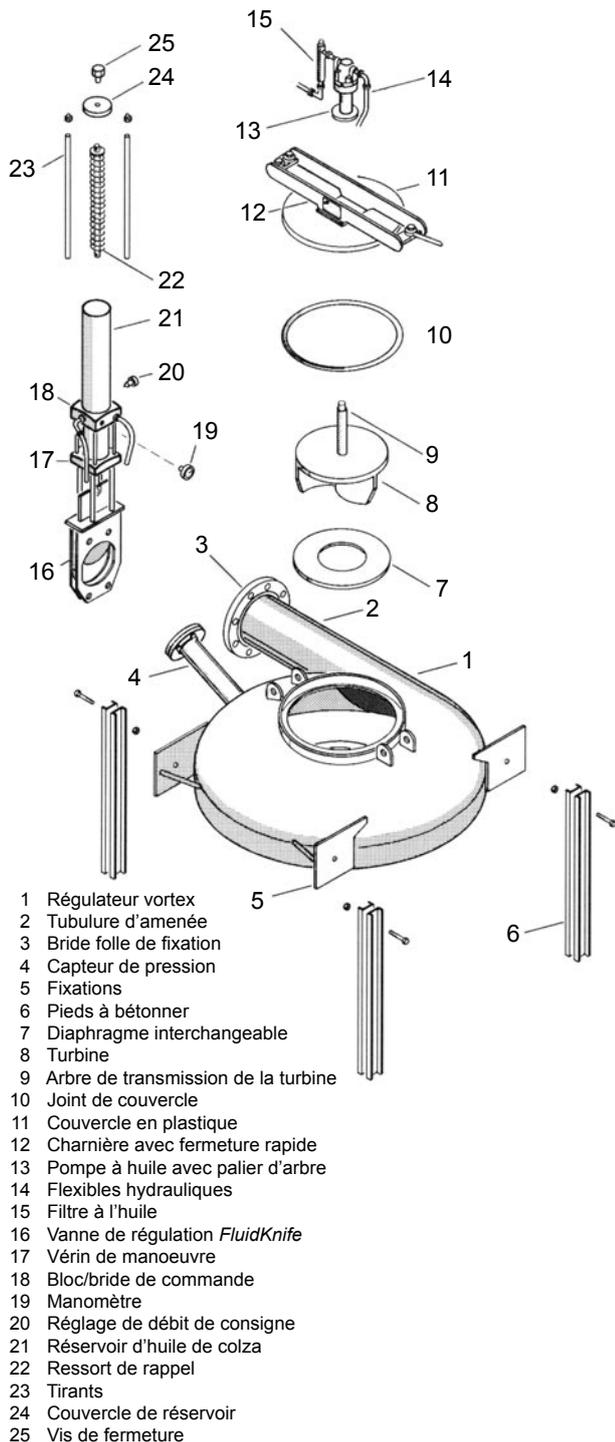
Vue éclatée d'un turbo-régulateur UFT-FluidTurbo
